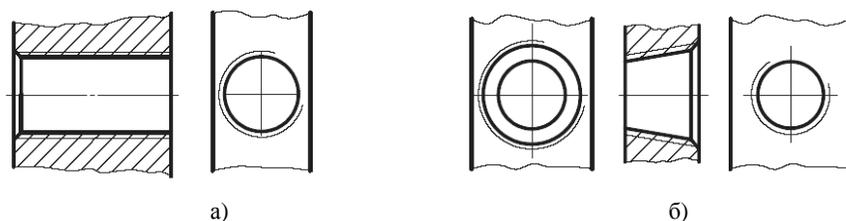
Изображение внутренней цилиндрической (а) и конической (б) резьбы
